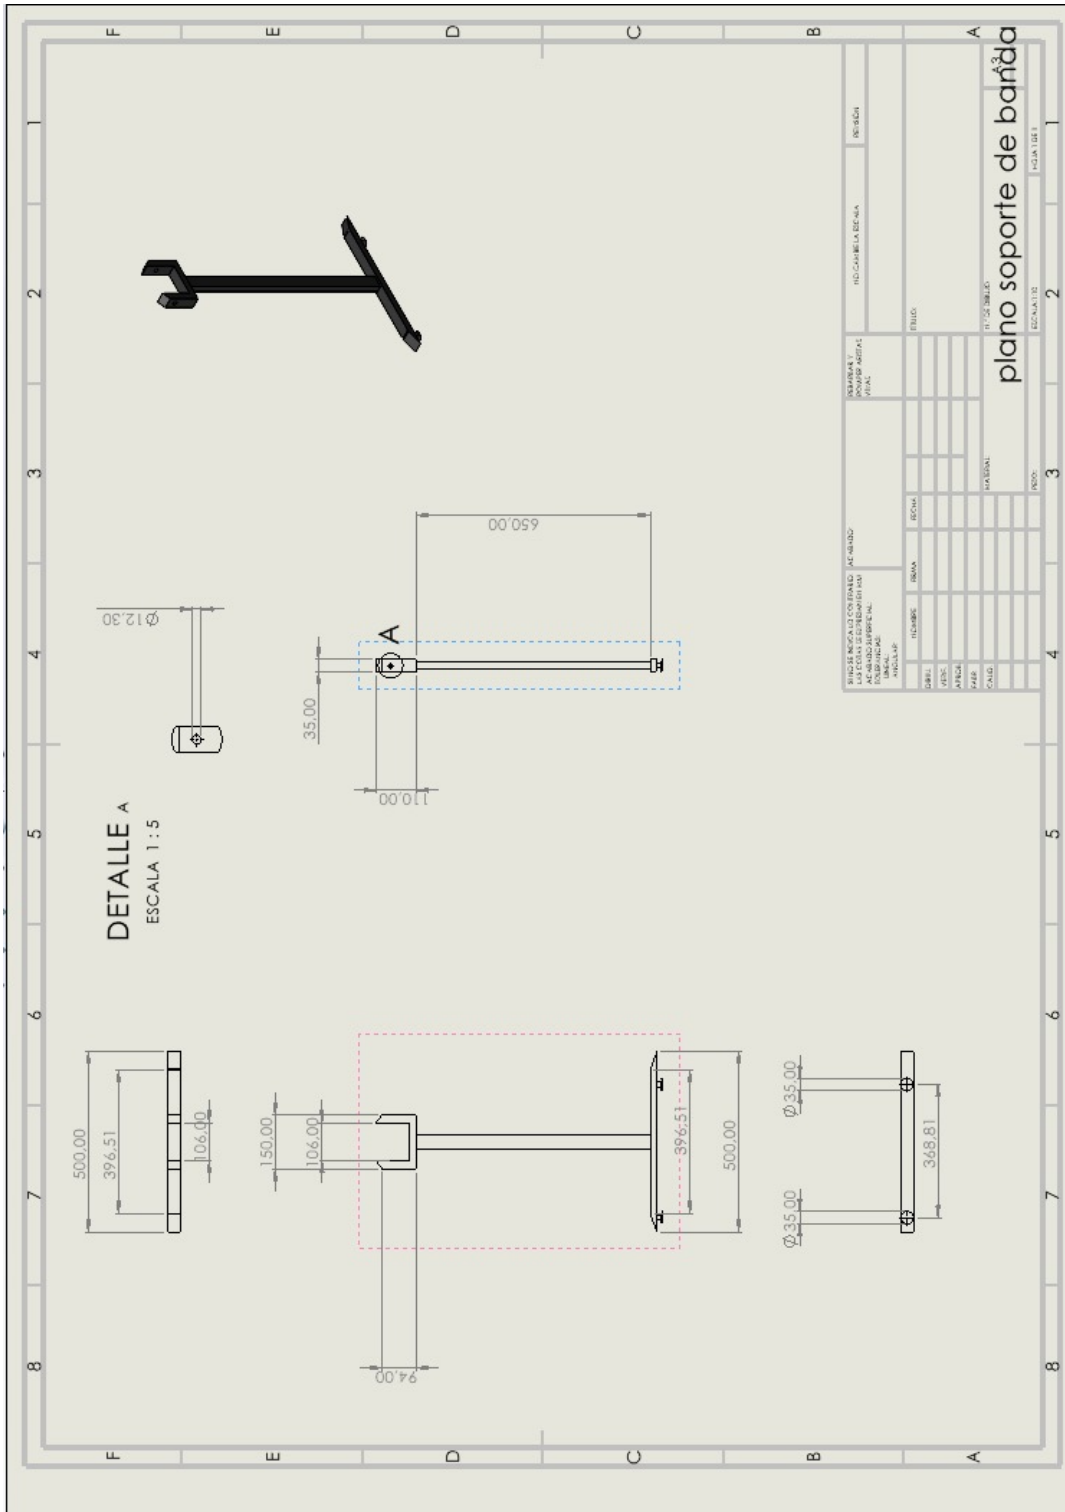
Plano soporte de banda. Fuente: Elaborado por autores.
